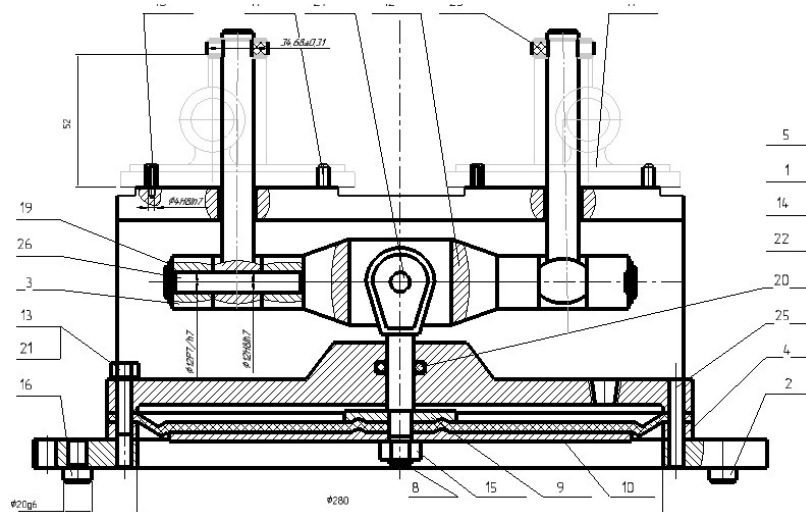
Схема верстатного пристрою для фрезерування
